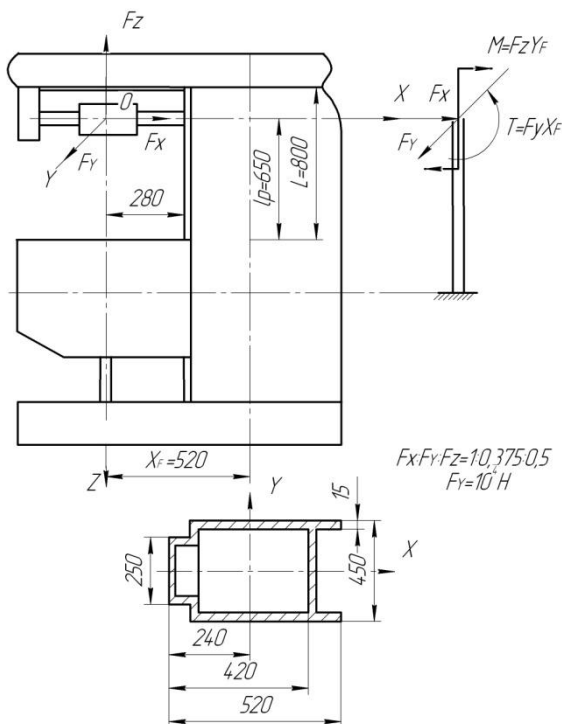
Расчетная схема стойки консольного горизонтально-фрезерного станка модели 6Н81
